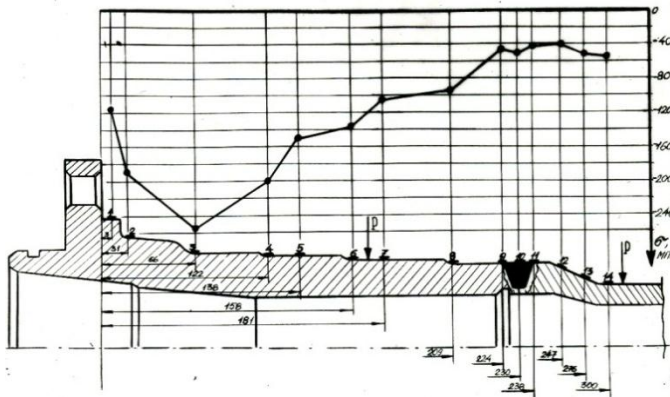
Схема размещения тензорезисторов и распределение напряжений в цапфе сварной конструкции из стали 18Х2Н4МА (при испытаниях на изгиб)
